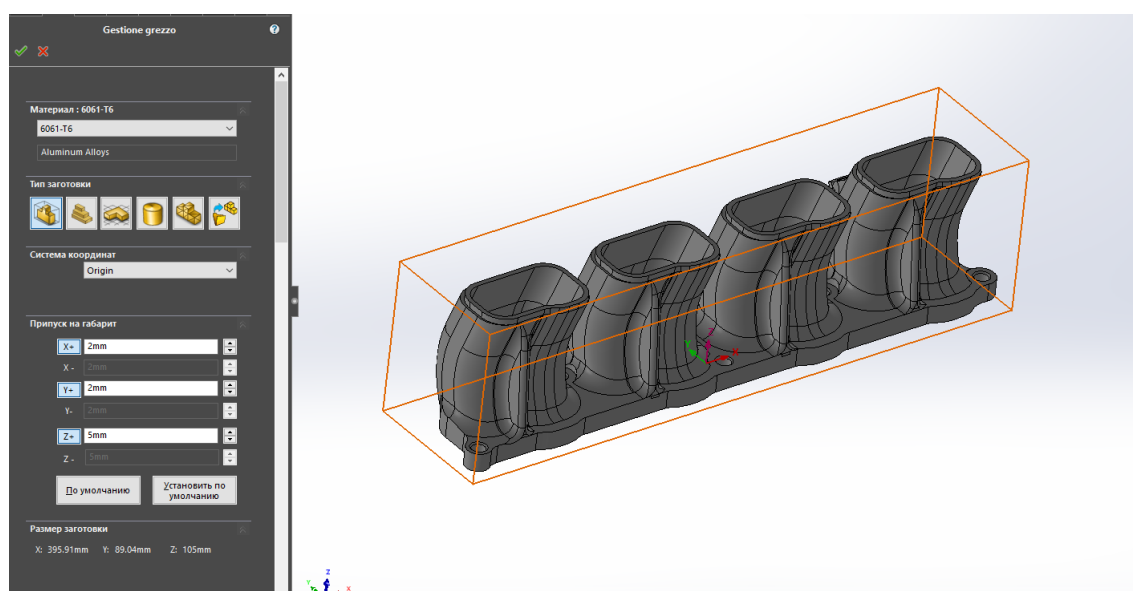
Заготовка для деталі «ранери» в SolidCAM
